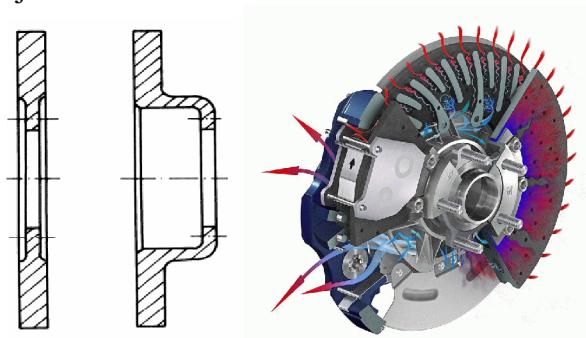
Kotoučová brzda s výkyvným třmenem [2]
